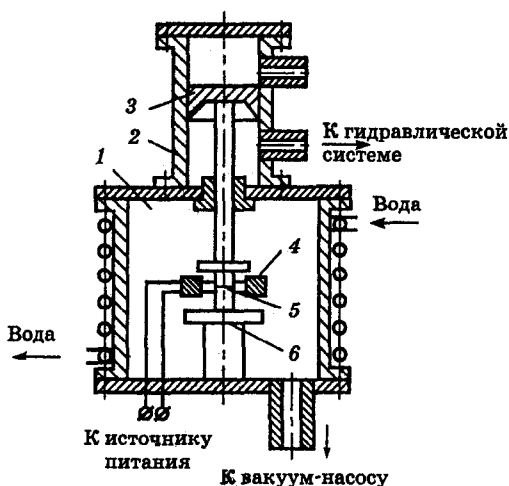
Принципиальная схема установки для диффузионной сварки в вакууме:
